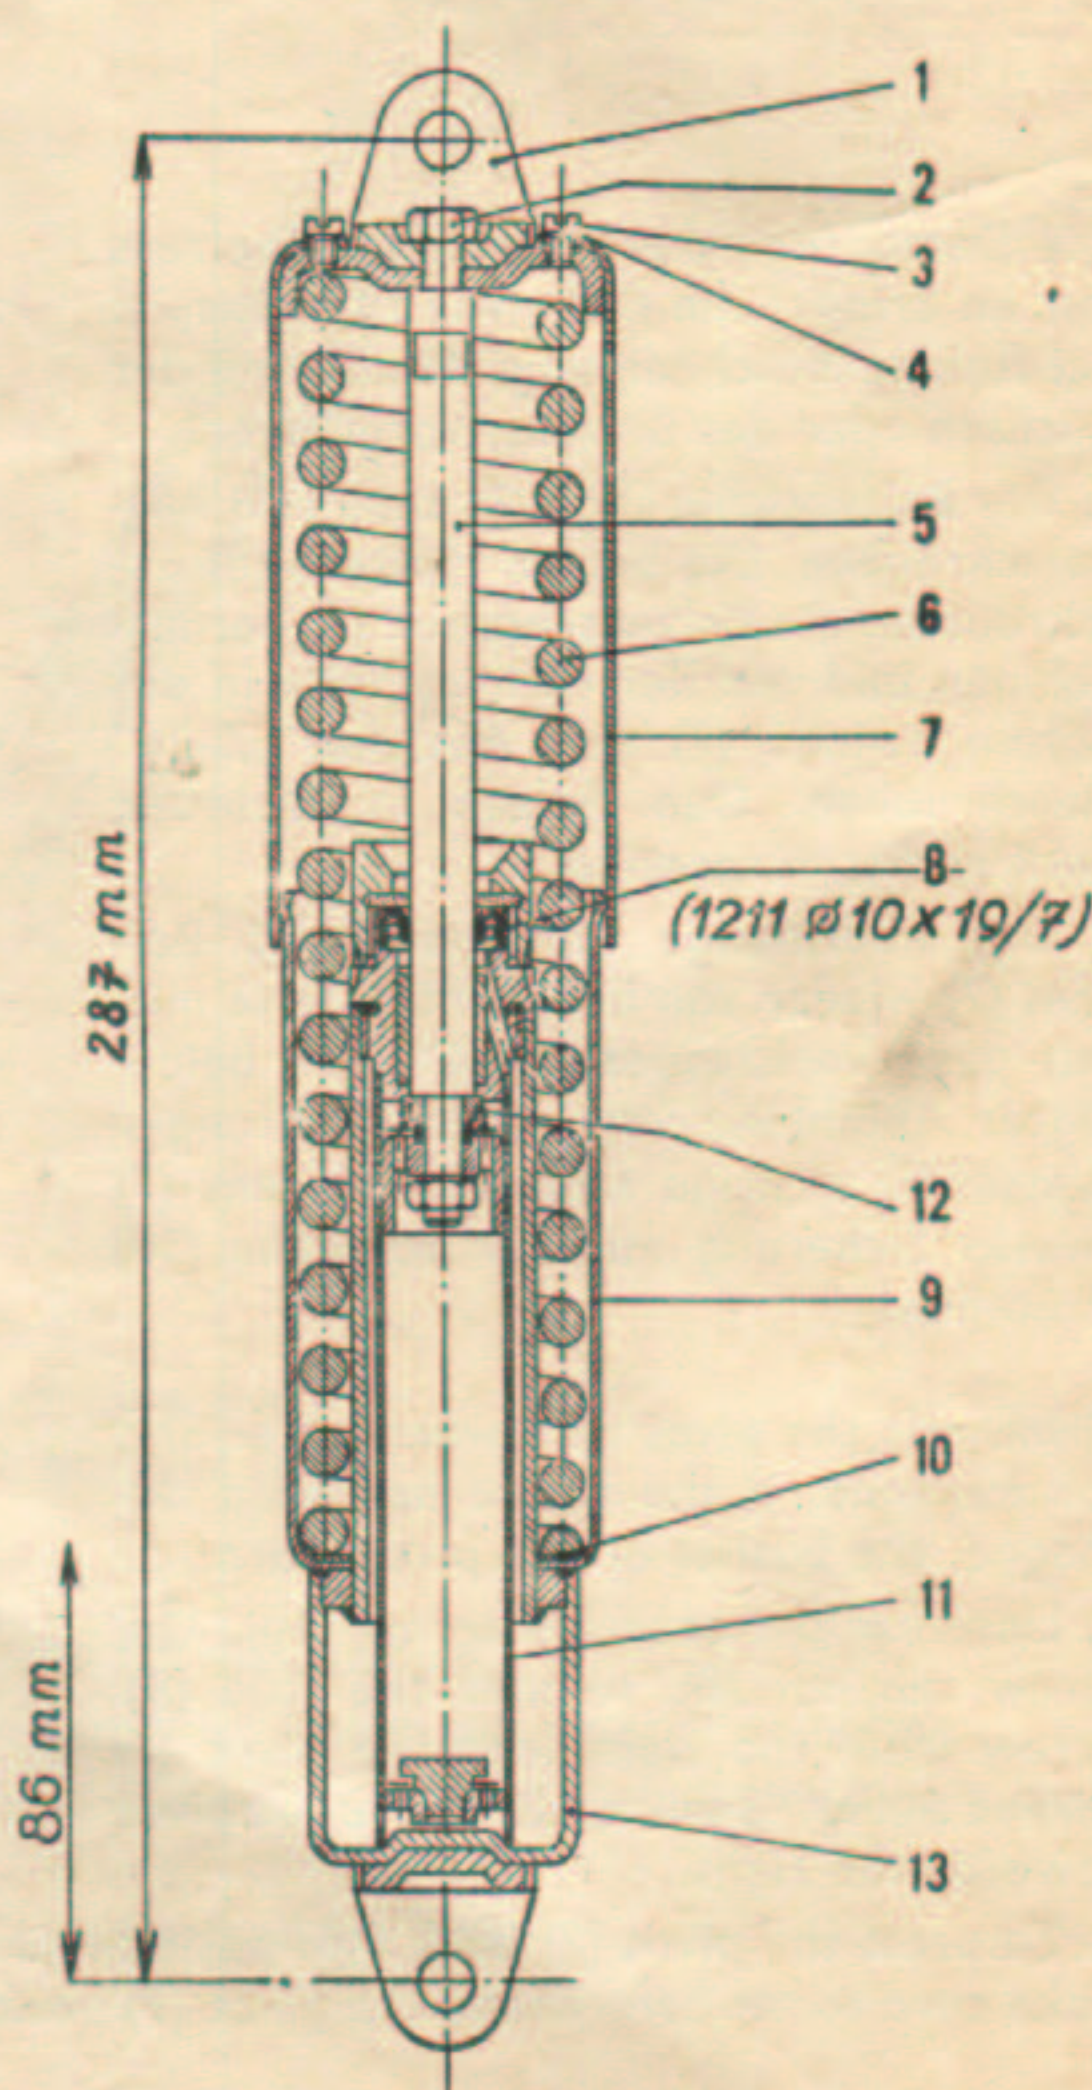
Stossdämpfer der Hinterradfederung I. (im Schnitt)
